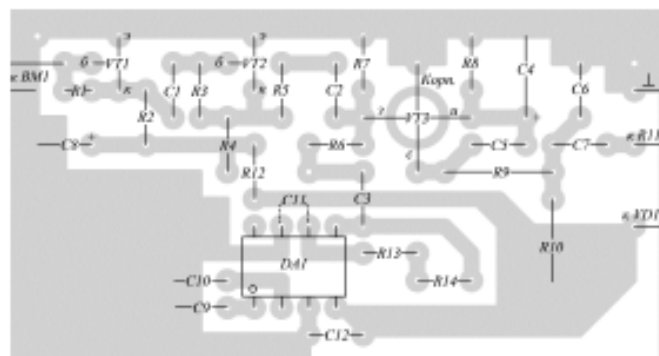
Ультразвуковой приёмник. Эскиз монтажной платы блока предварительного усилителя - гетеродина - смесителя. Вид со стороны установки деталей
